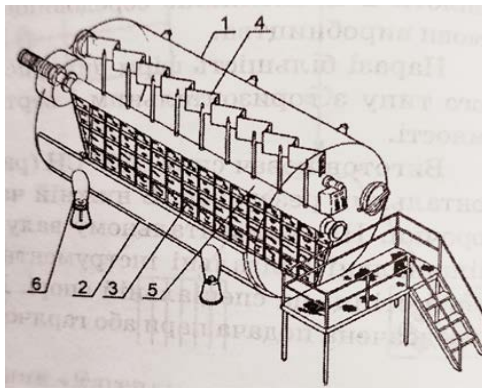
Горизонтальний виготовлювач сиру фірми «Пасілак» [11]: 1 – корпус; 2 – теплообмінна сорочка; 3 – різальний інструмент; 4 – лопатка; 5 – вал
